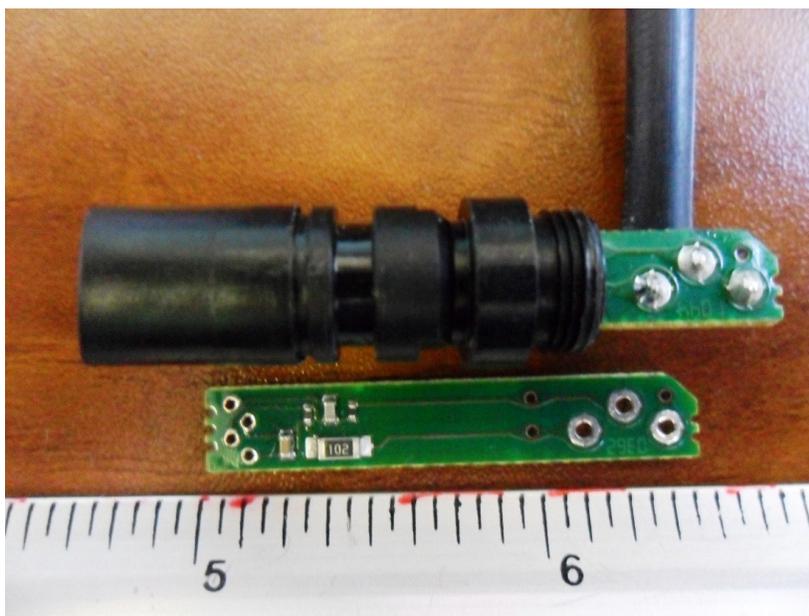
Sensor de transmisión automática completo, y vista de la tablilla electrónica con componentes soldados que encuentra encapsulada en el interior de la coraza de plástico sellado.
